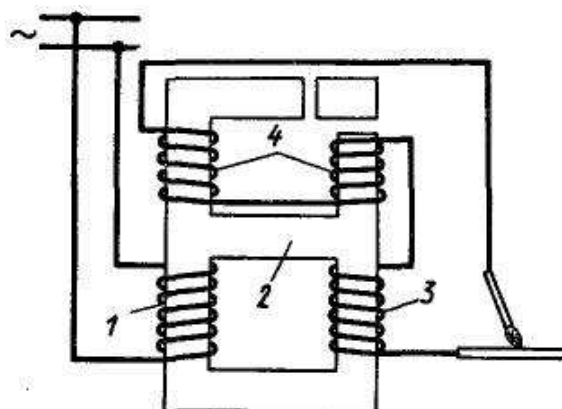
Электромагнитная схема сварочного трансформатора с встроенным реактором
